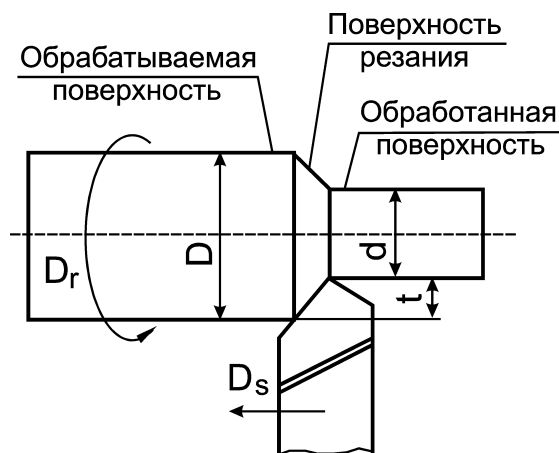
Основные поверхности заготовки и основные движения, необходимые для осуществления процесса резания при точении
